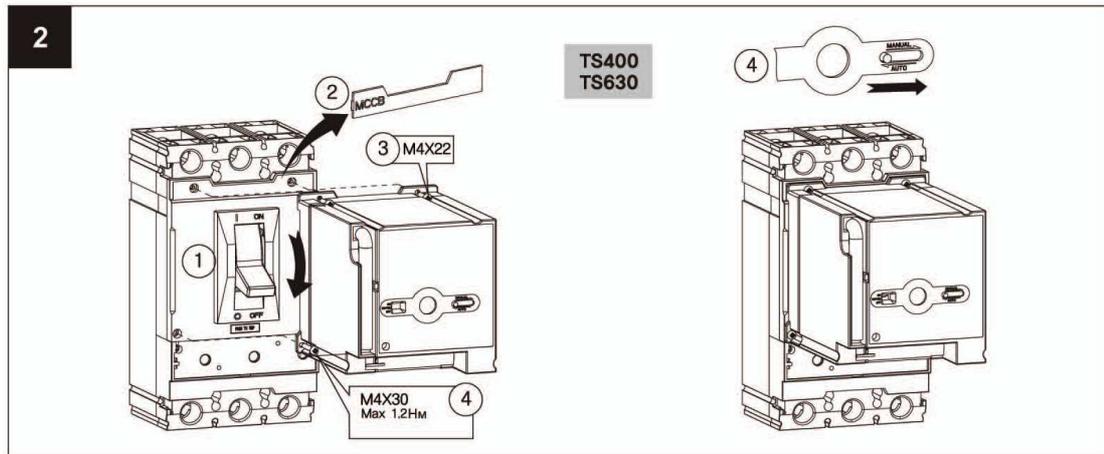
Установка моторного привода на выключатели TS400 и TS630
